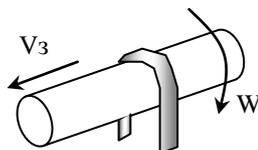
Пример перемещения заготовки на одновалковом магазине
